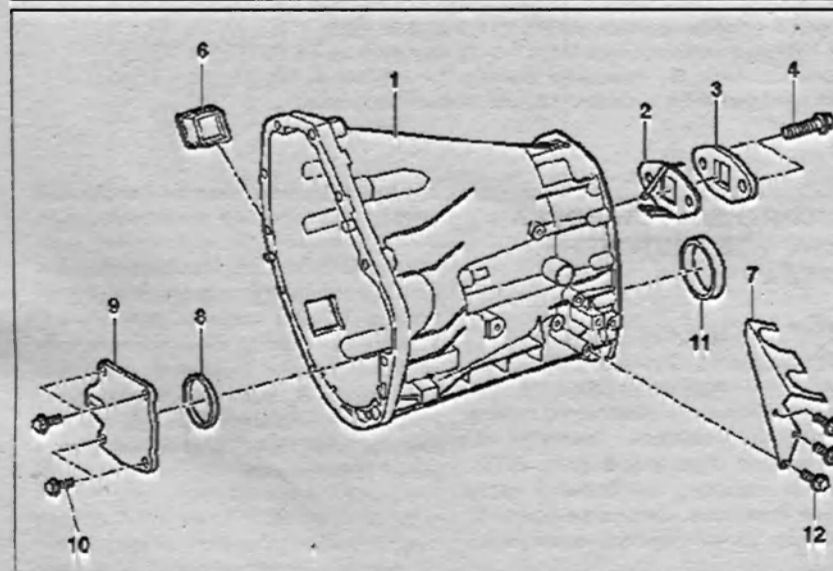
б. Разборка и сборка передней части корпуса МКПП 711.620/621:
